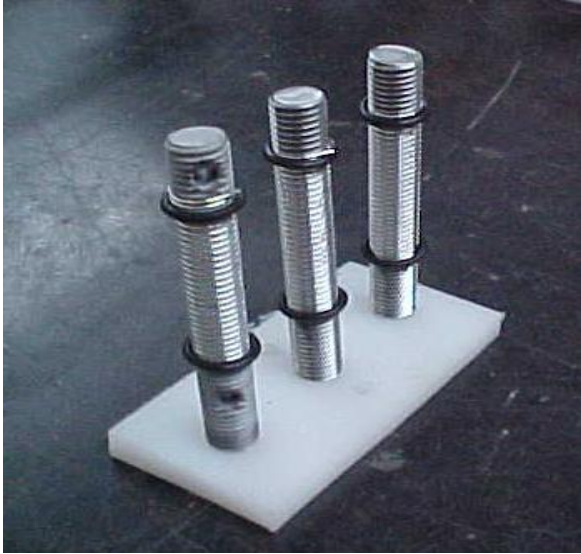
Ensamblaje :”alambre sobre tornillo”
